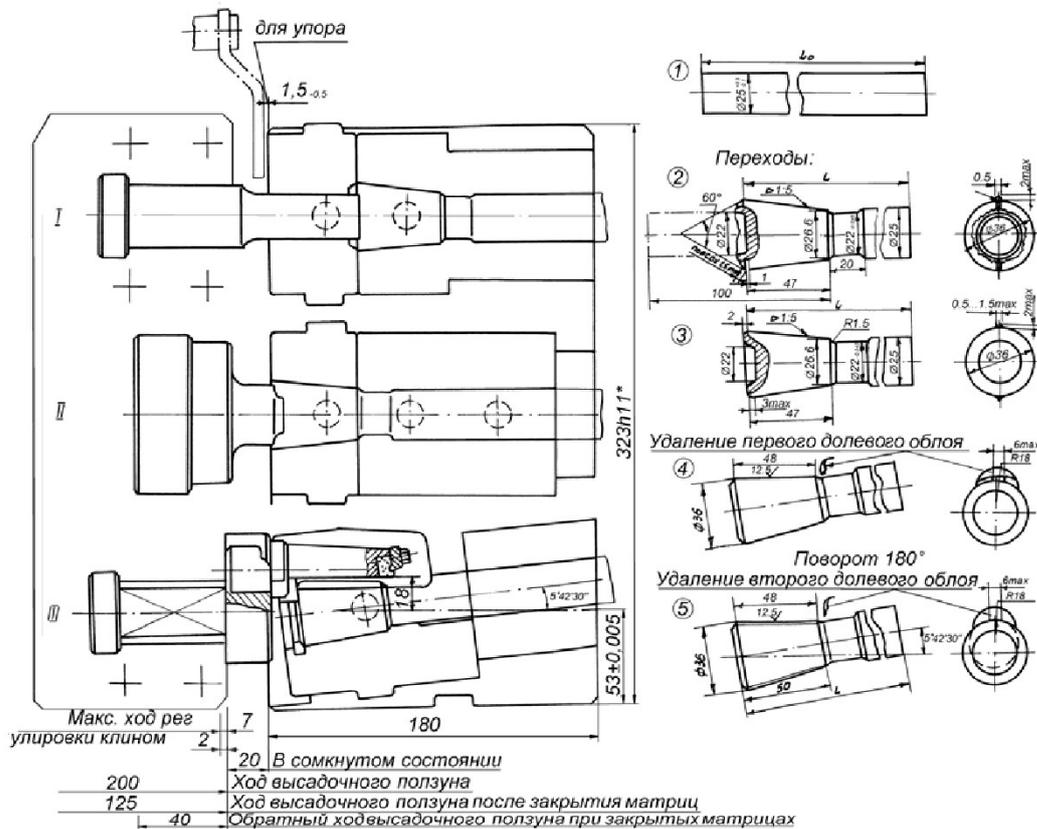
Наладка ГKM160 для штамповки штанги: 1- заготовка: круг
